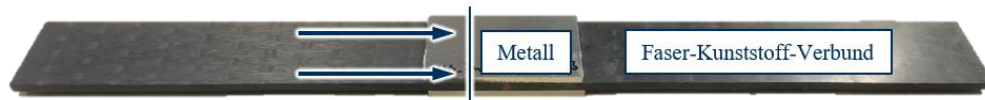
DLS-Probe mit Schnittansicht für die Mikroskopie
